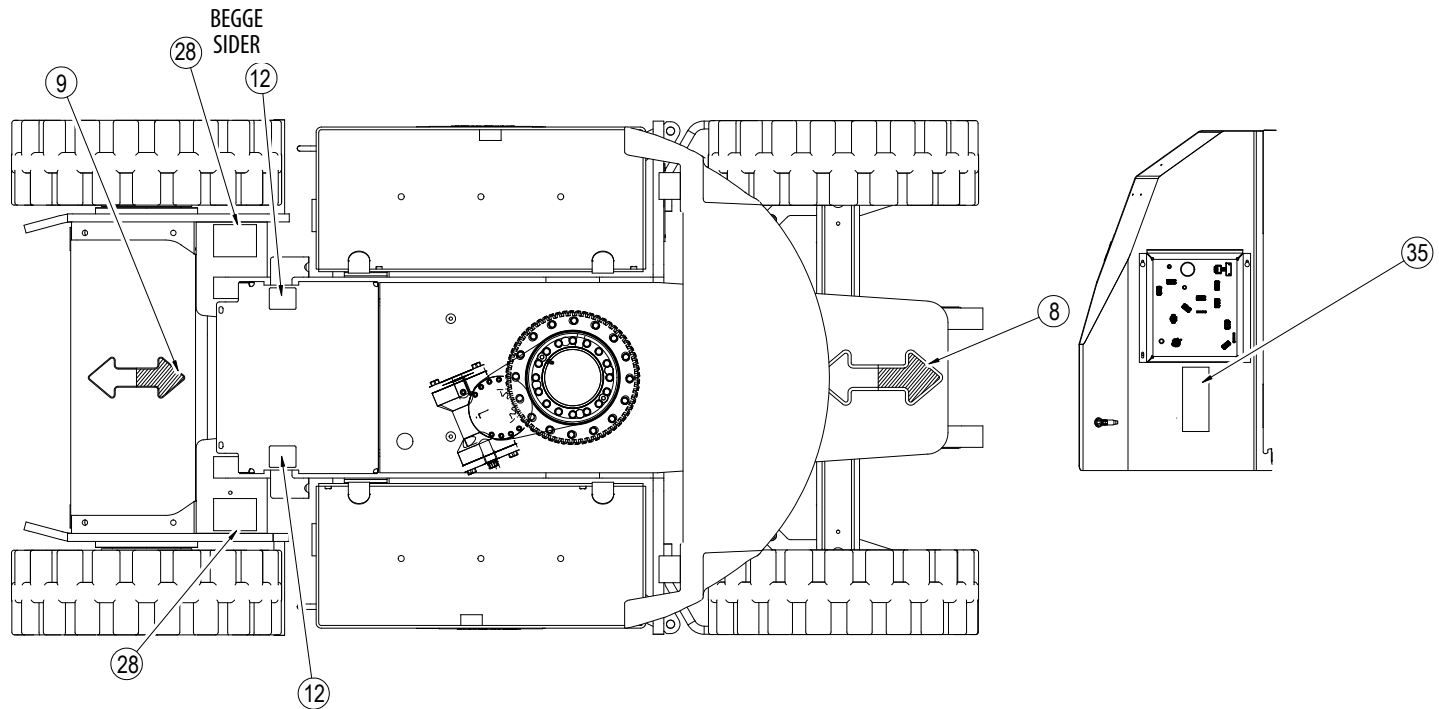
Japan, merkeplassering – ark 2 av 5
